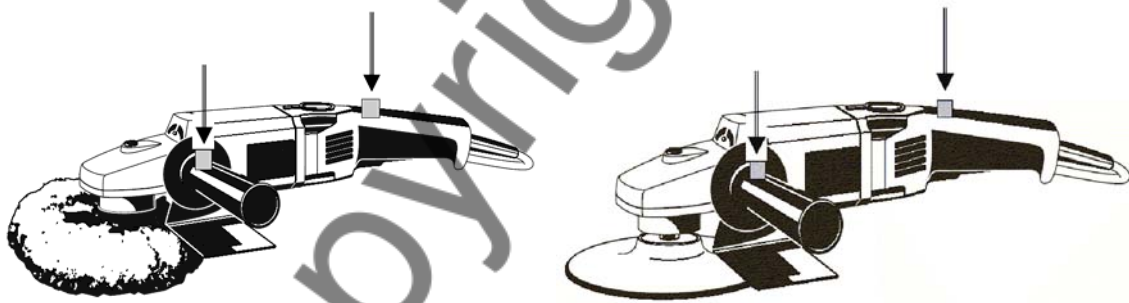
Lage der Schwingungsaufnehmer für Polierer und Schleifer mit Schleifblatt
